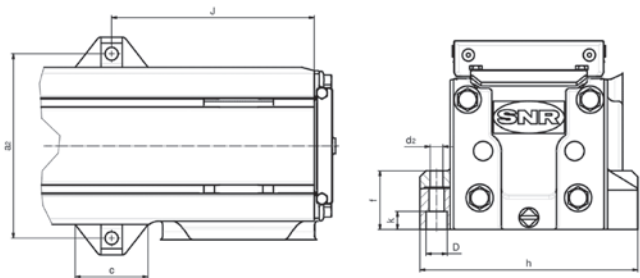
Abmessungen Befestigungselement AXF
